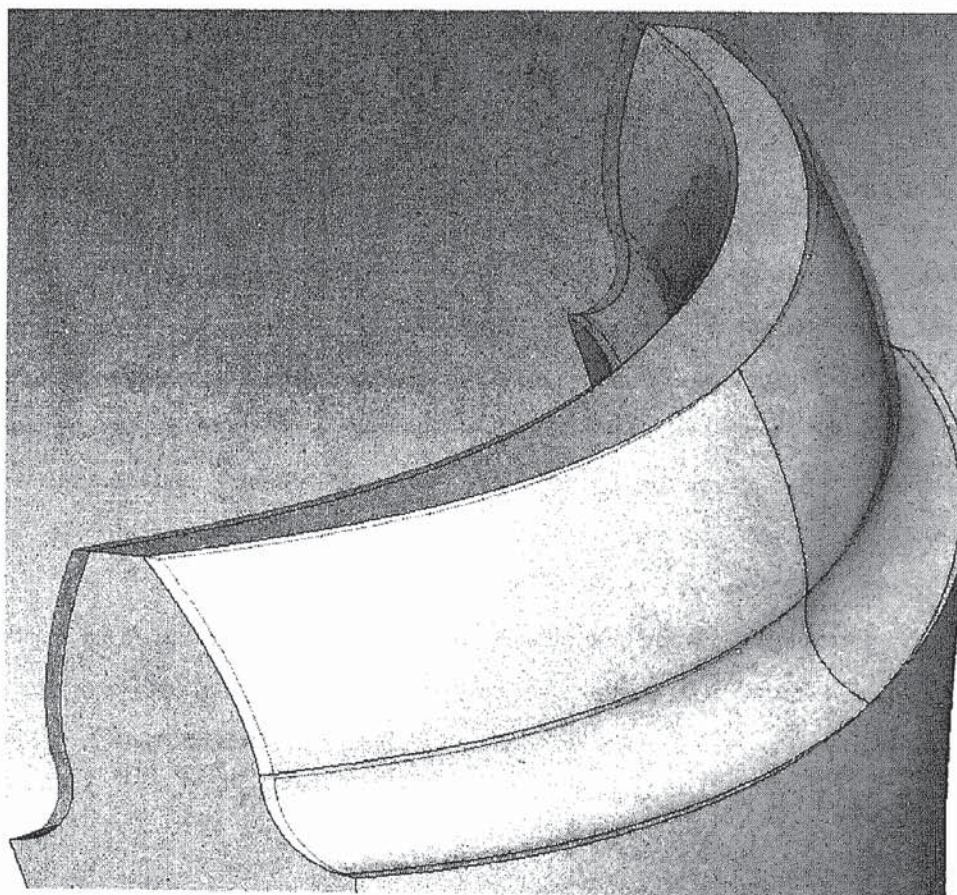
Бочкообразный зуб арочного цилиндрического колеса
